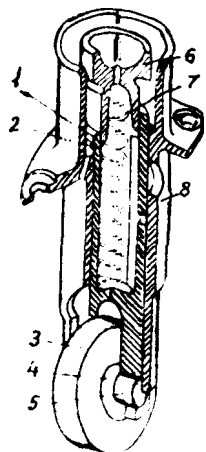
Узел толкателя: 1—толкатель; 2—предохранительное кольцо; 3—ролик; 4—втулка ролика; 5—ось ролика; 6—шаровое гнездо; 7—пружина; 8—направляющая
